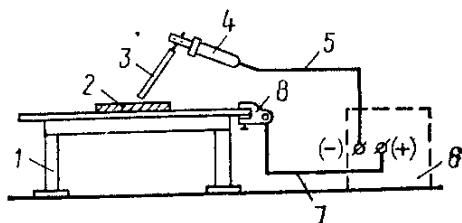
Схема поста для ручной дуговой сварки:
